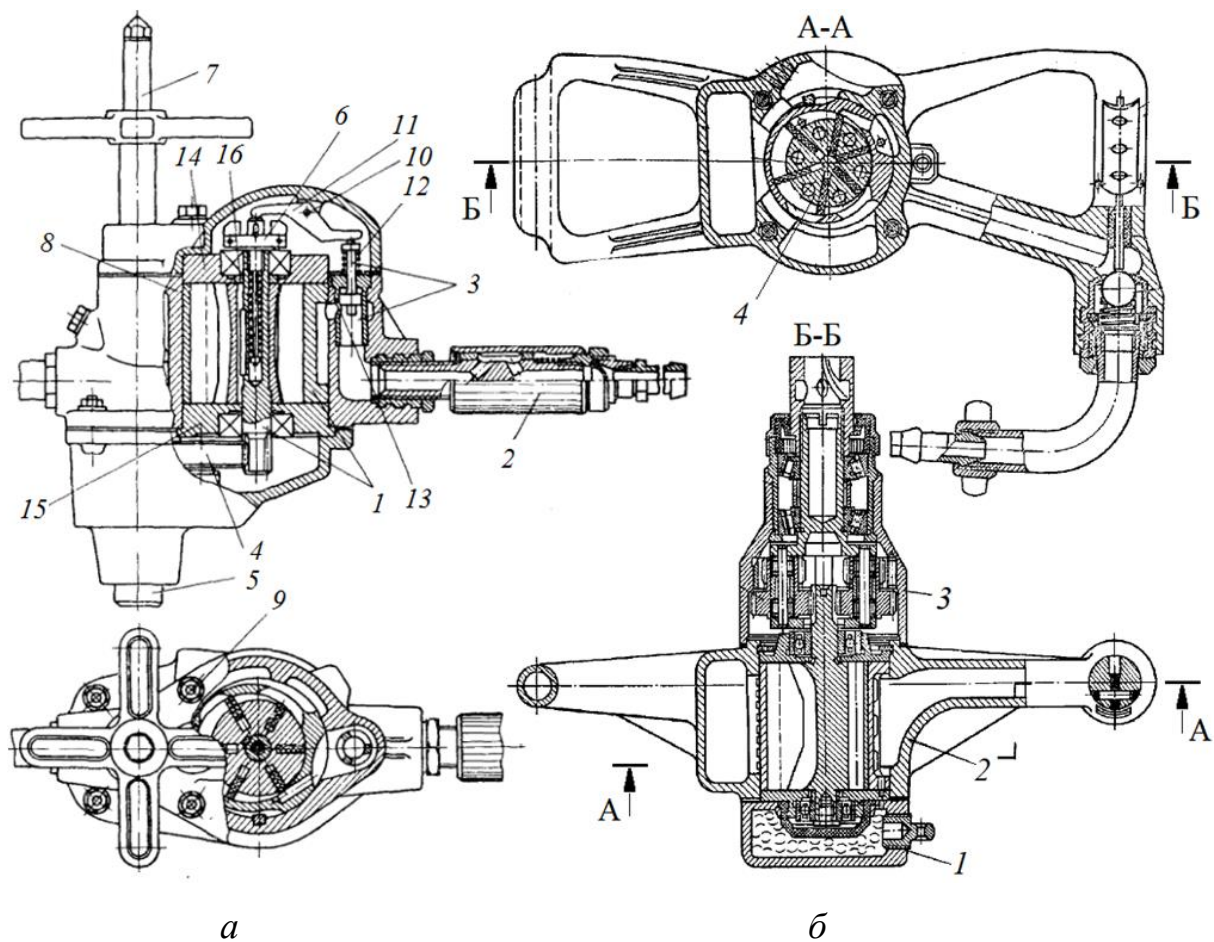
Свердлильний пневматичний інструмент:
